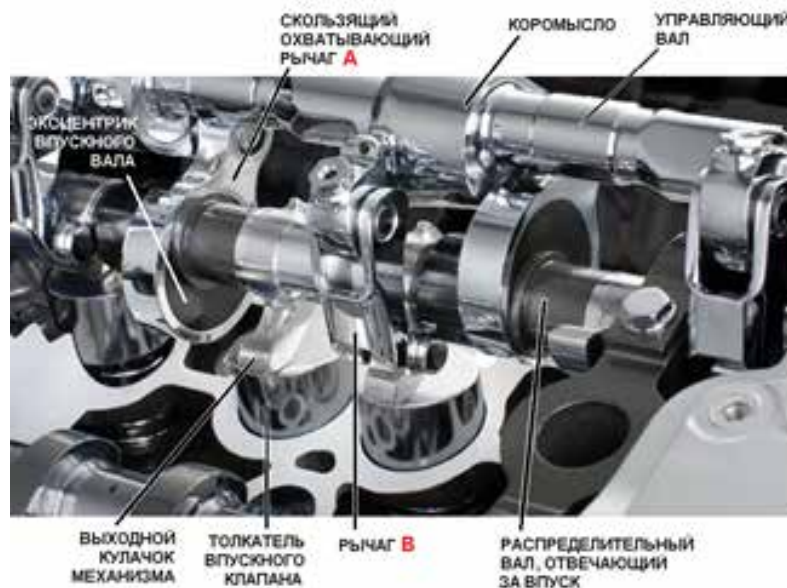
На снимке хорошо виден эксцентриковый вал распределительный вал, отвечающий за открытие впускных клапанов, и охватывающий скользящий рычаг, передающий качающее движение на коромысло, надетое на эксцентриковый управляющий вал механизма VVEL. Выходные кулачки механизма надеты на распределительный вал, но не связаны с ним, используя вал, как ось, на которой эти кулачки могут свободно совершать колебательные движения; источник: Nissan
